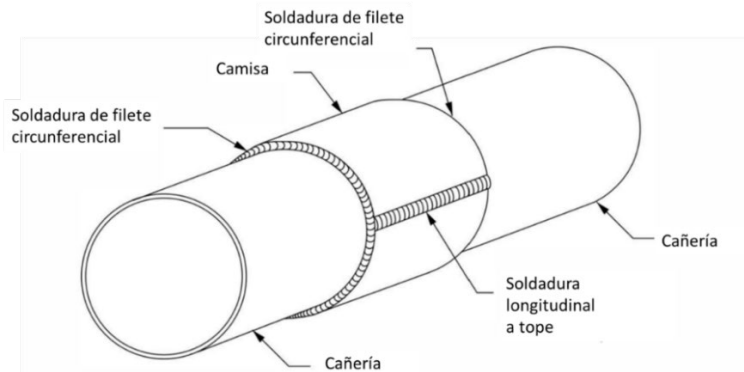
Refuerzo tipo B. (ASME PCC-2, 2022, Figura 206-1.1.2-1)
